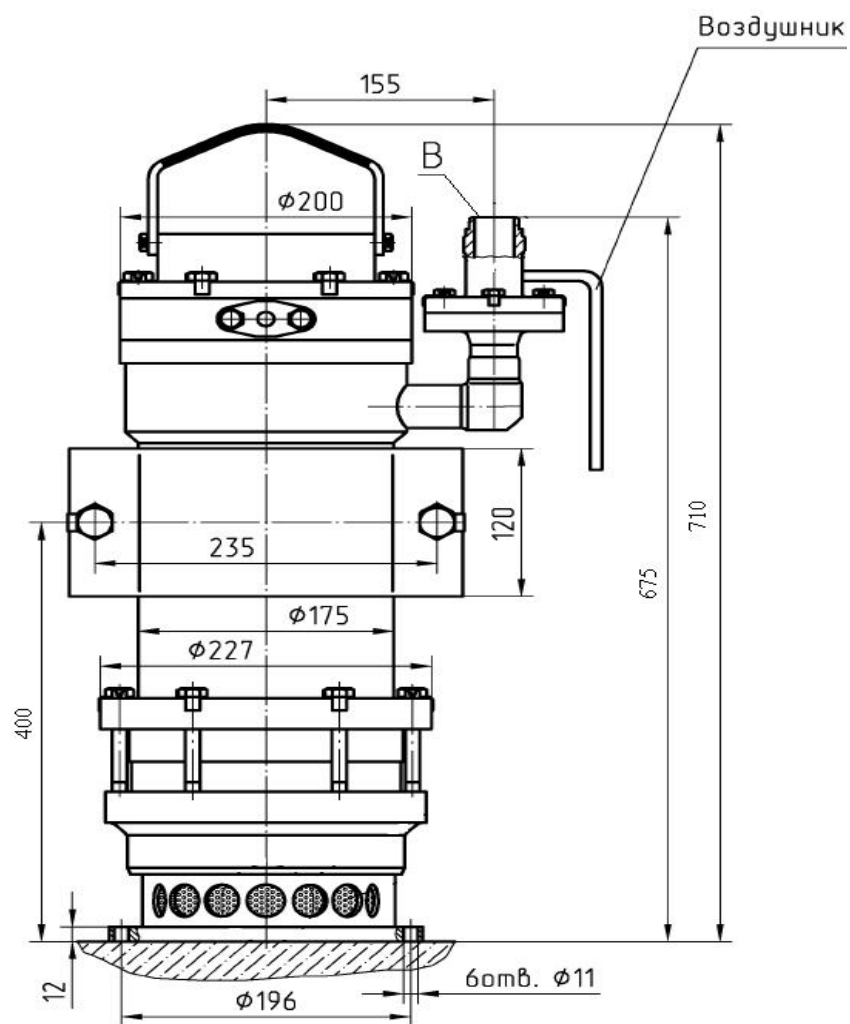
Габаритный чертеж насоса бака боросодержащих дренажей
